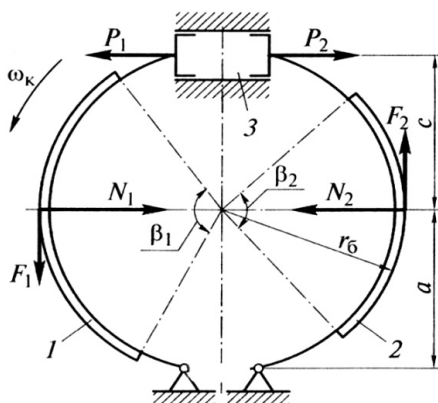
Схема барабанного тормозного механизма с гидравлическим приводом, равными приводными силами и односторонним расположением фиксированных опор: 1 и 2 — тормозные колодки, 3 — колесный цилиндр
